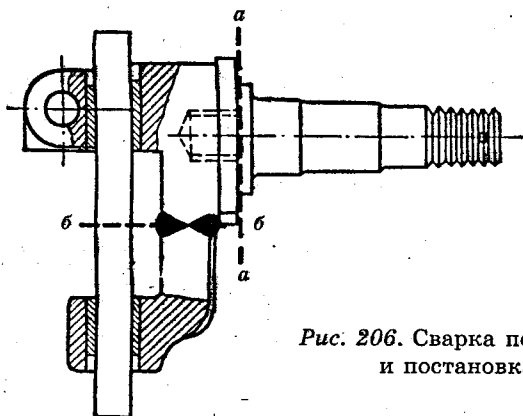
Сварка поворотного кулака и постановка новой оси
